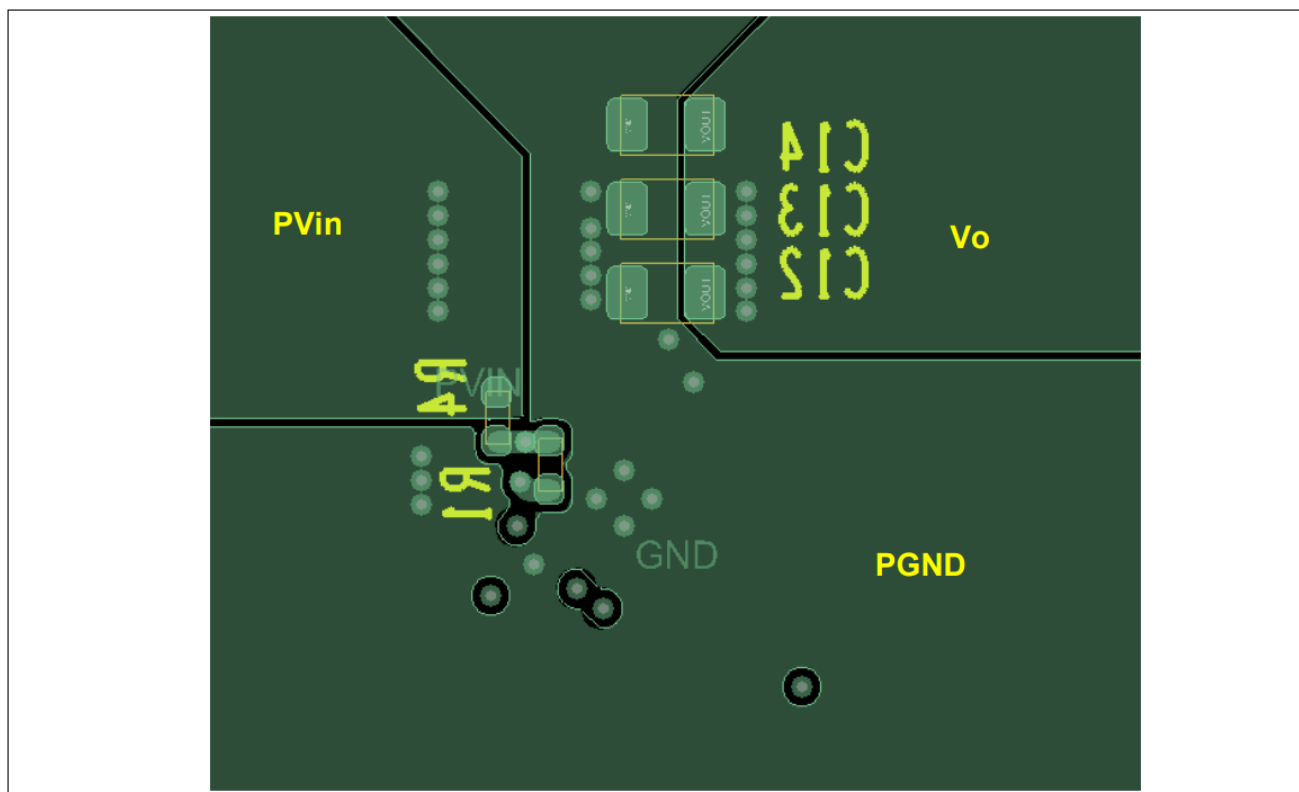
IRDC3883 Demo Board Layer – Bottom Layer
